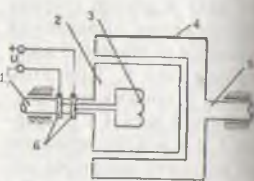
Муфта скольжения: 1-ведущий вал; 2-индуктор; 3-обмотка; 4-якорь; 5-контактные кольца; 6-ведомый вал.
